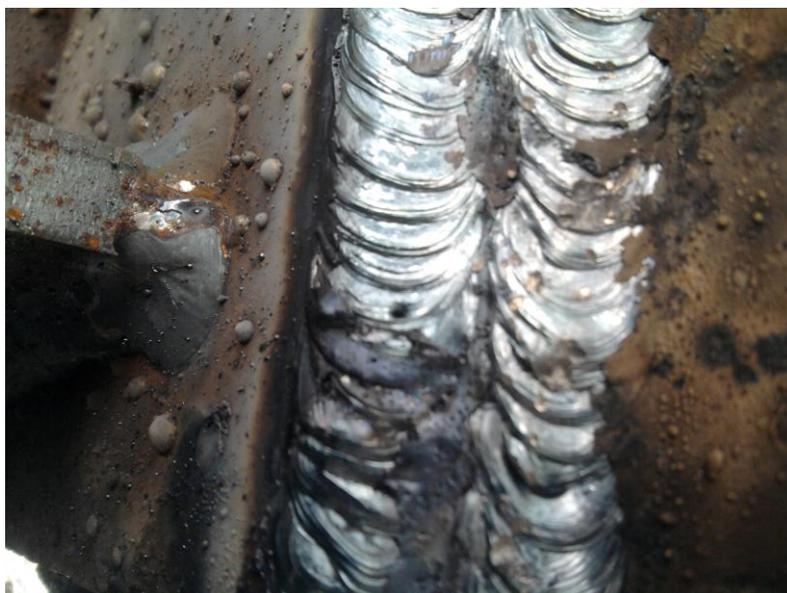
Дефекты сварного шва в виде поры, западания между валиками и грубой чешуйчатости.
